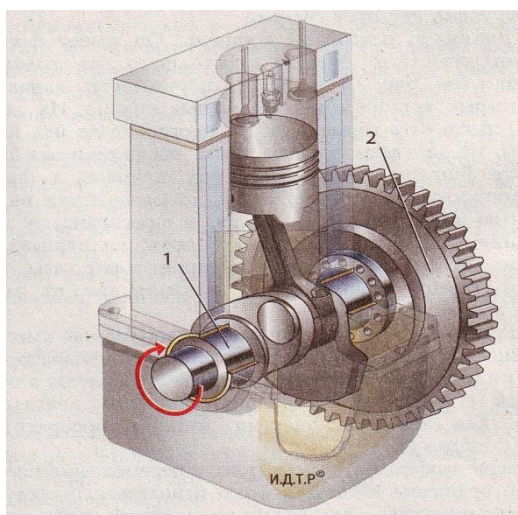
6 – Расположение маховика коленчатого вала:
